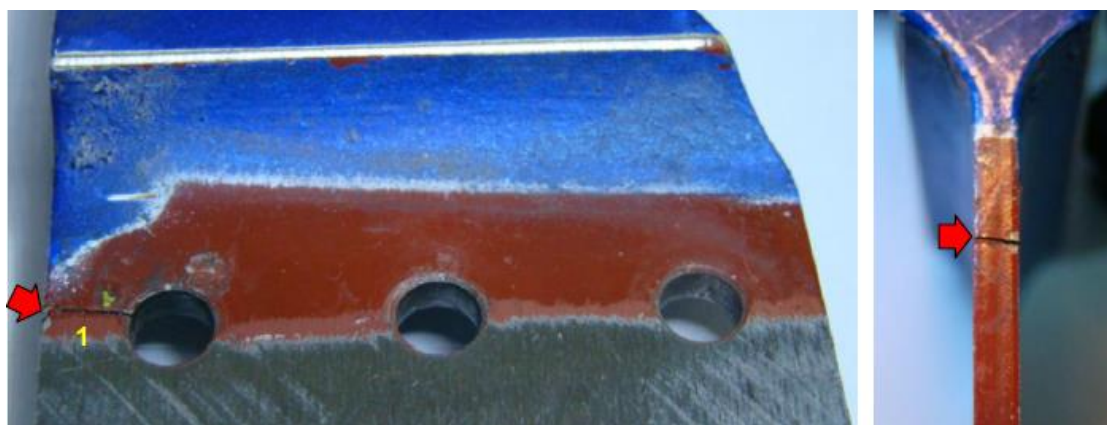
Fisura en el herraje izquierdo. Fuente: investigación JST
